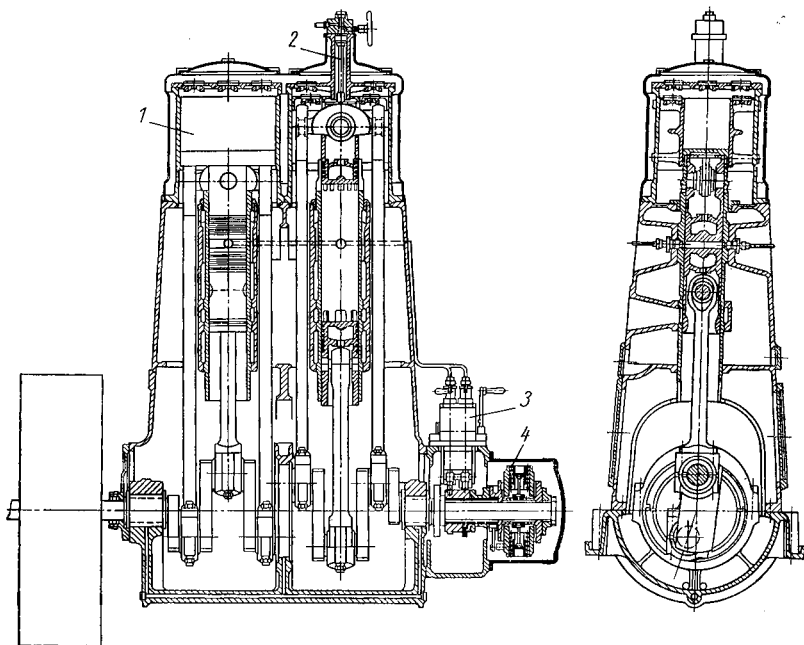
Двигатель небольшой мощности с противоположно движущимися поршнями и одним коленчатым валом:
